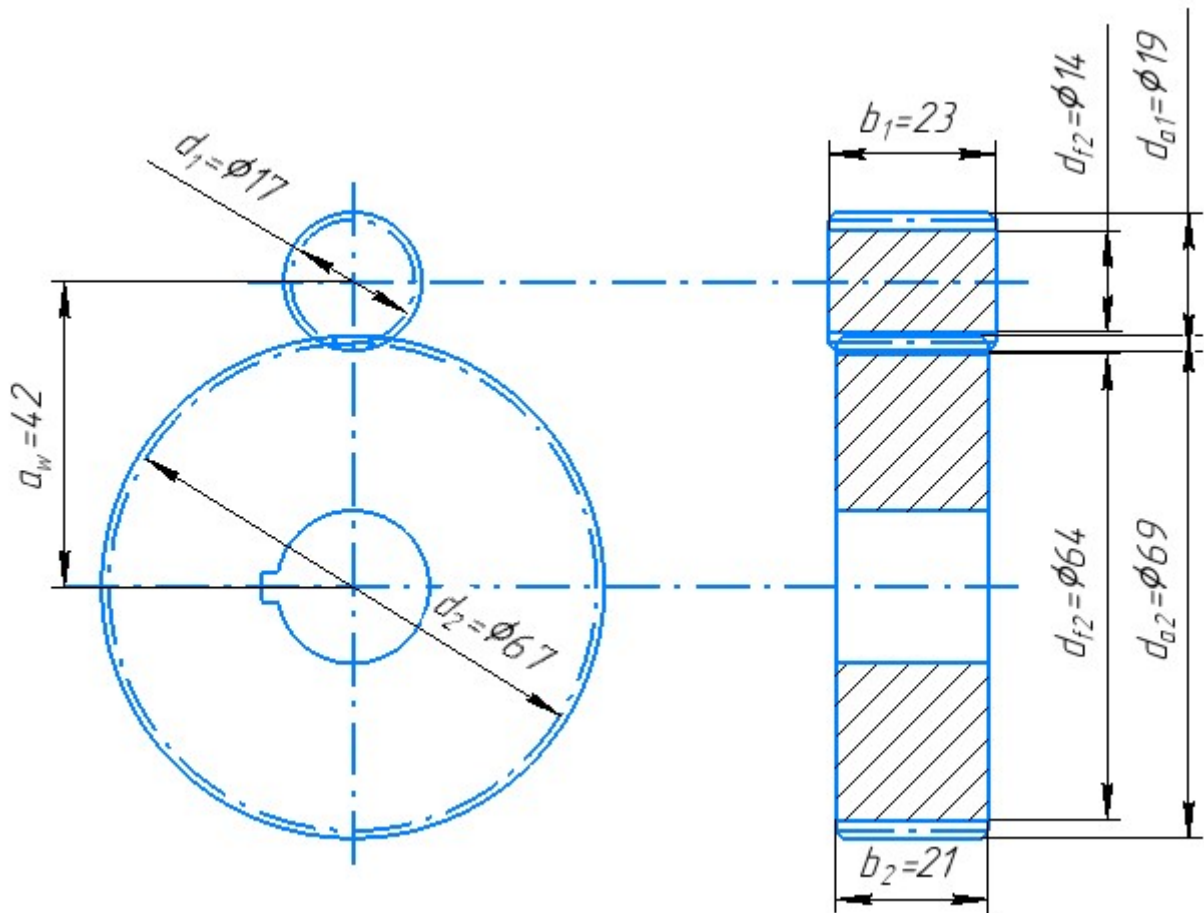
Параметри косозубої зубчастої циліндричної передачі
